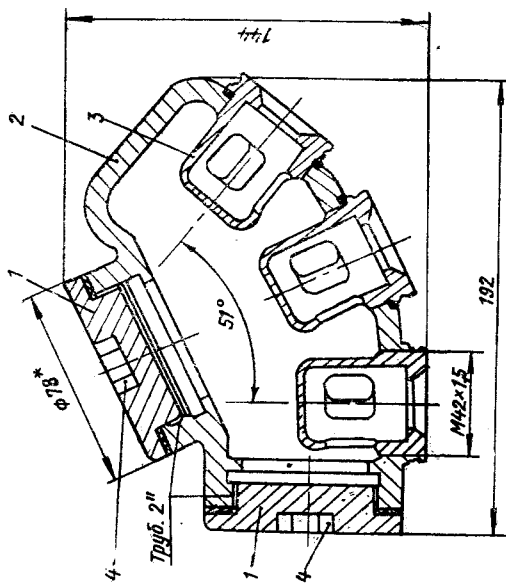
Насадок комбинированный центробежный трехвставочный НКЦ-3 (черт. С1312, ВНИИПО):
